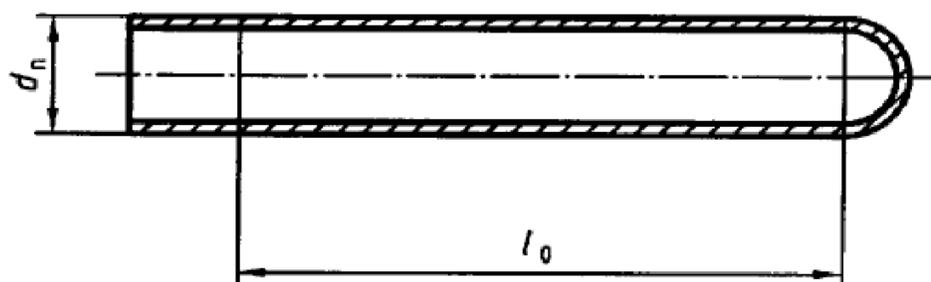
Образец в форме трубы, изготовленный литьем под давлением
